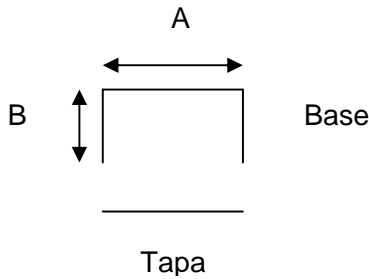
Croquis canal metàl·lica amb dimensions A i B.
